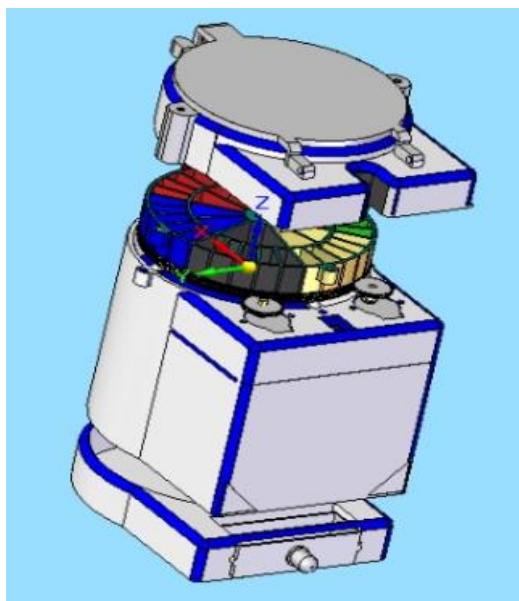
DISEÑO COMPLETO DEL DISPENSADOR
